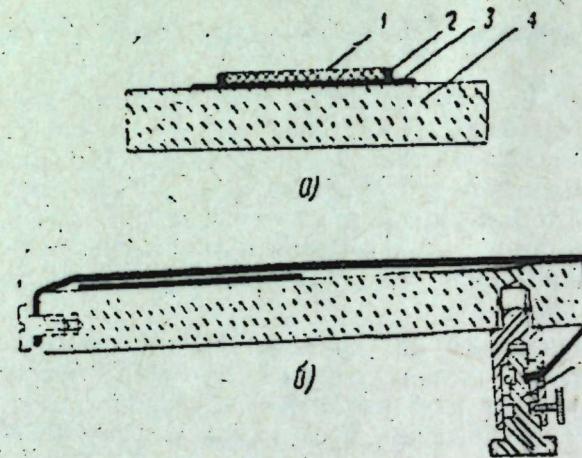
Схематическое изображение приспособления для изготовления поглотителя.
